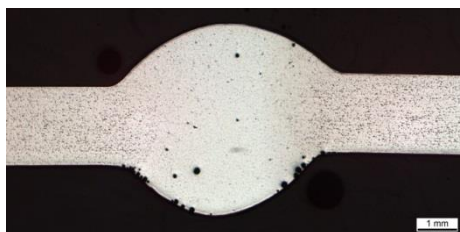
Микрошлиф сварного шва, $V = 4$ м/мин
